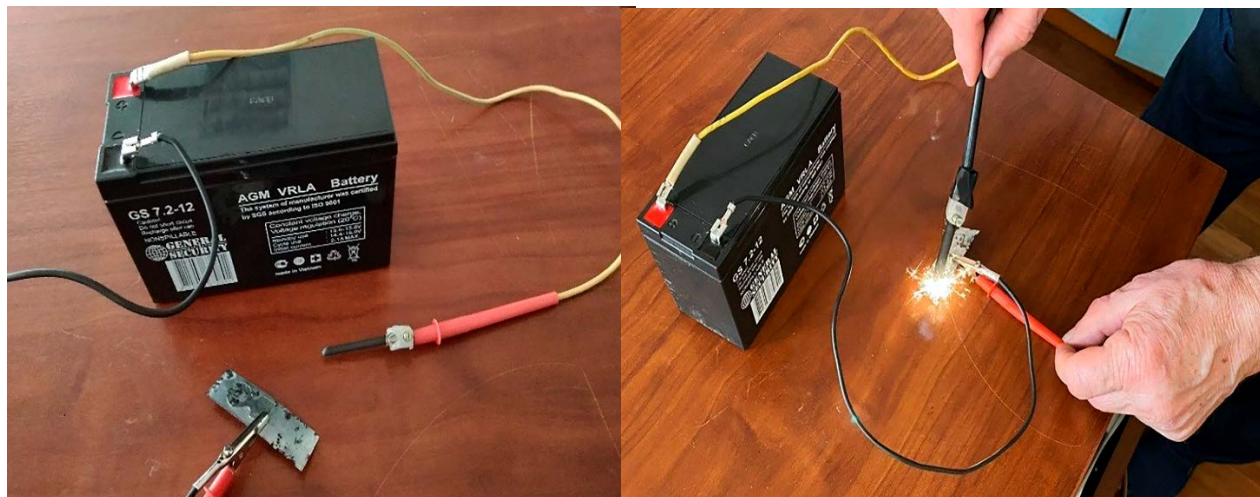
Самодельное устройство для точечной сварки
